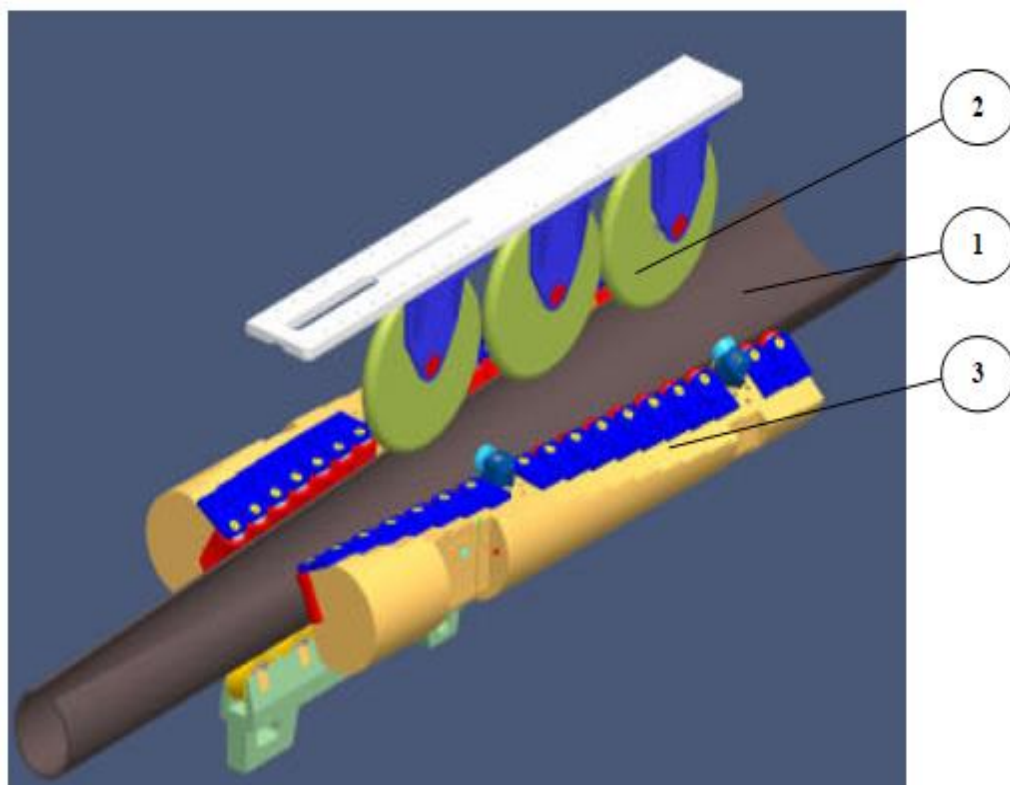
Способ линейной СТА-F (Central Tool Adjustment Forming) формовки [16, 19]:
